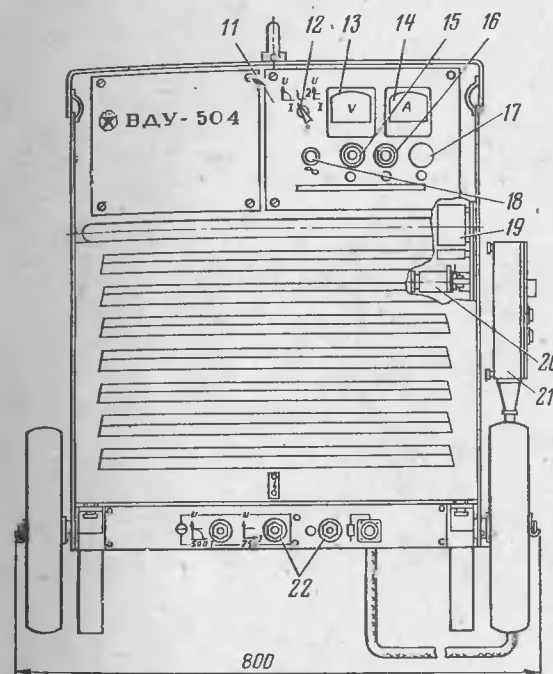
Сварочный выпрямитель ВДУ-504.
